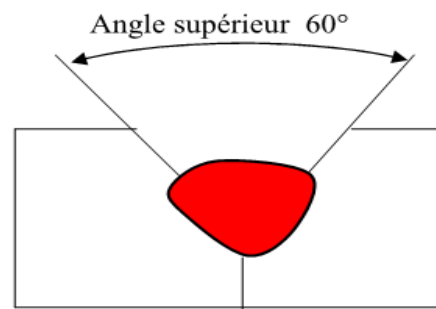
Forme du cordon lors d'un soudage rapide
